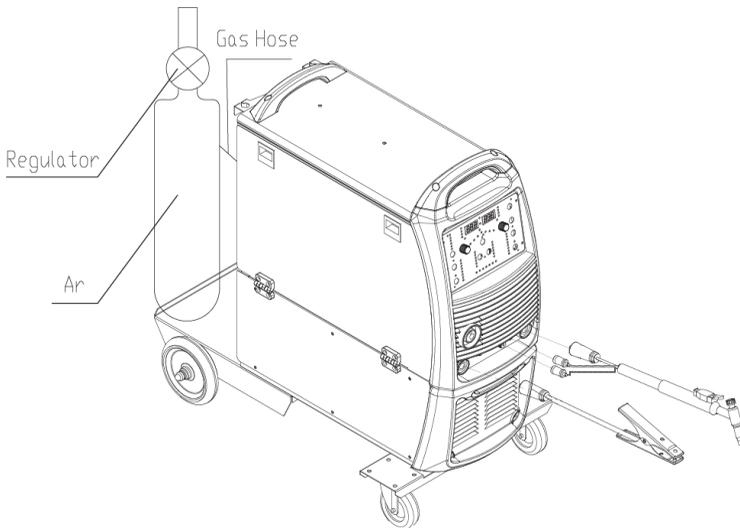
Схематичное подключение при сварке TIG
